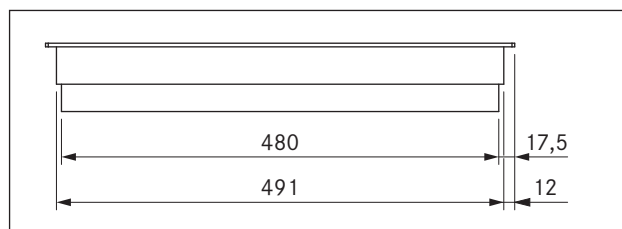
CKCH dimensioni apparecchio vista laterale
